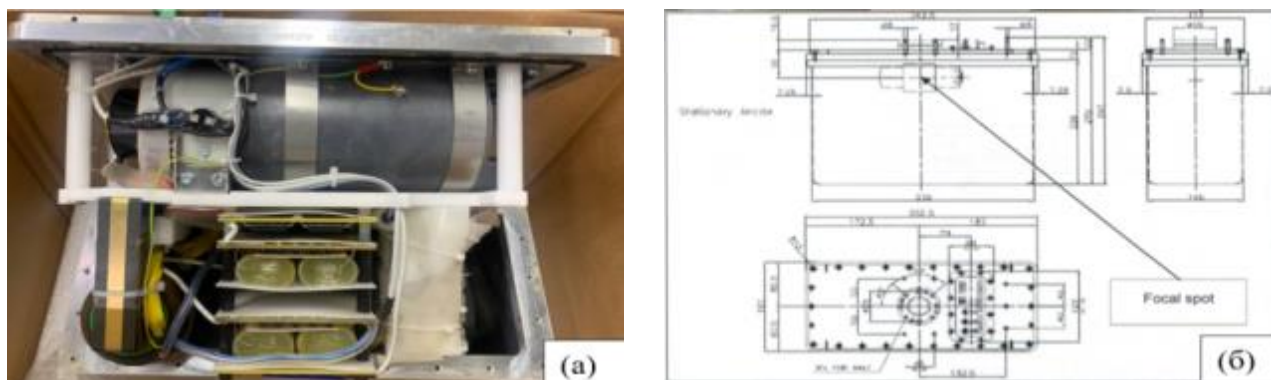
а – фото внутренних компонентов моноблока, б – схема корпуса излучателя.
